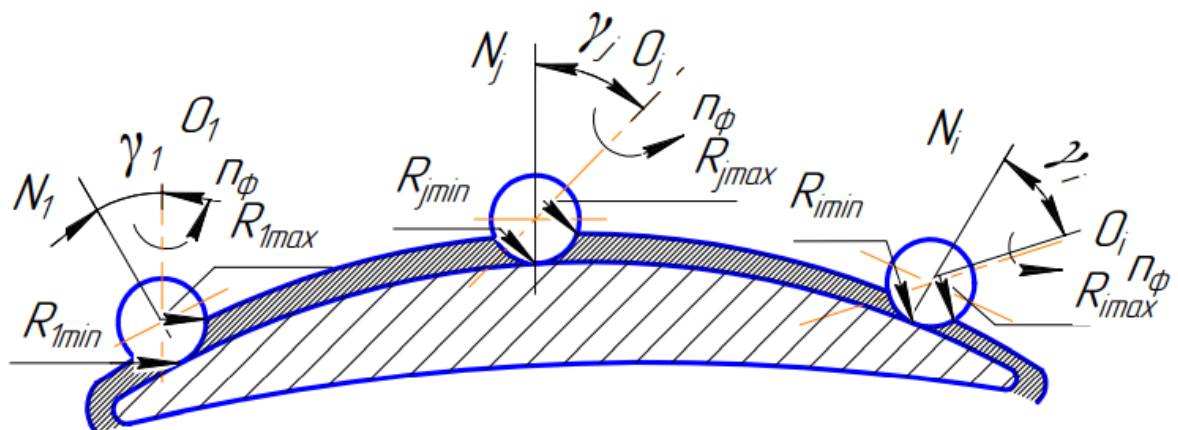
Схема положений инструмента со сферической режущей частью на поверхности заготовки лопатки
